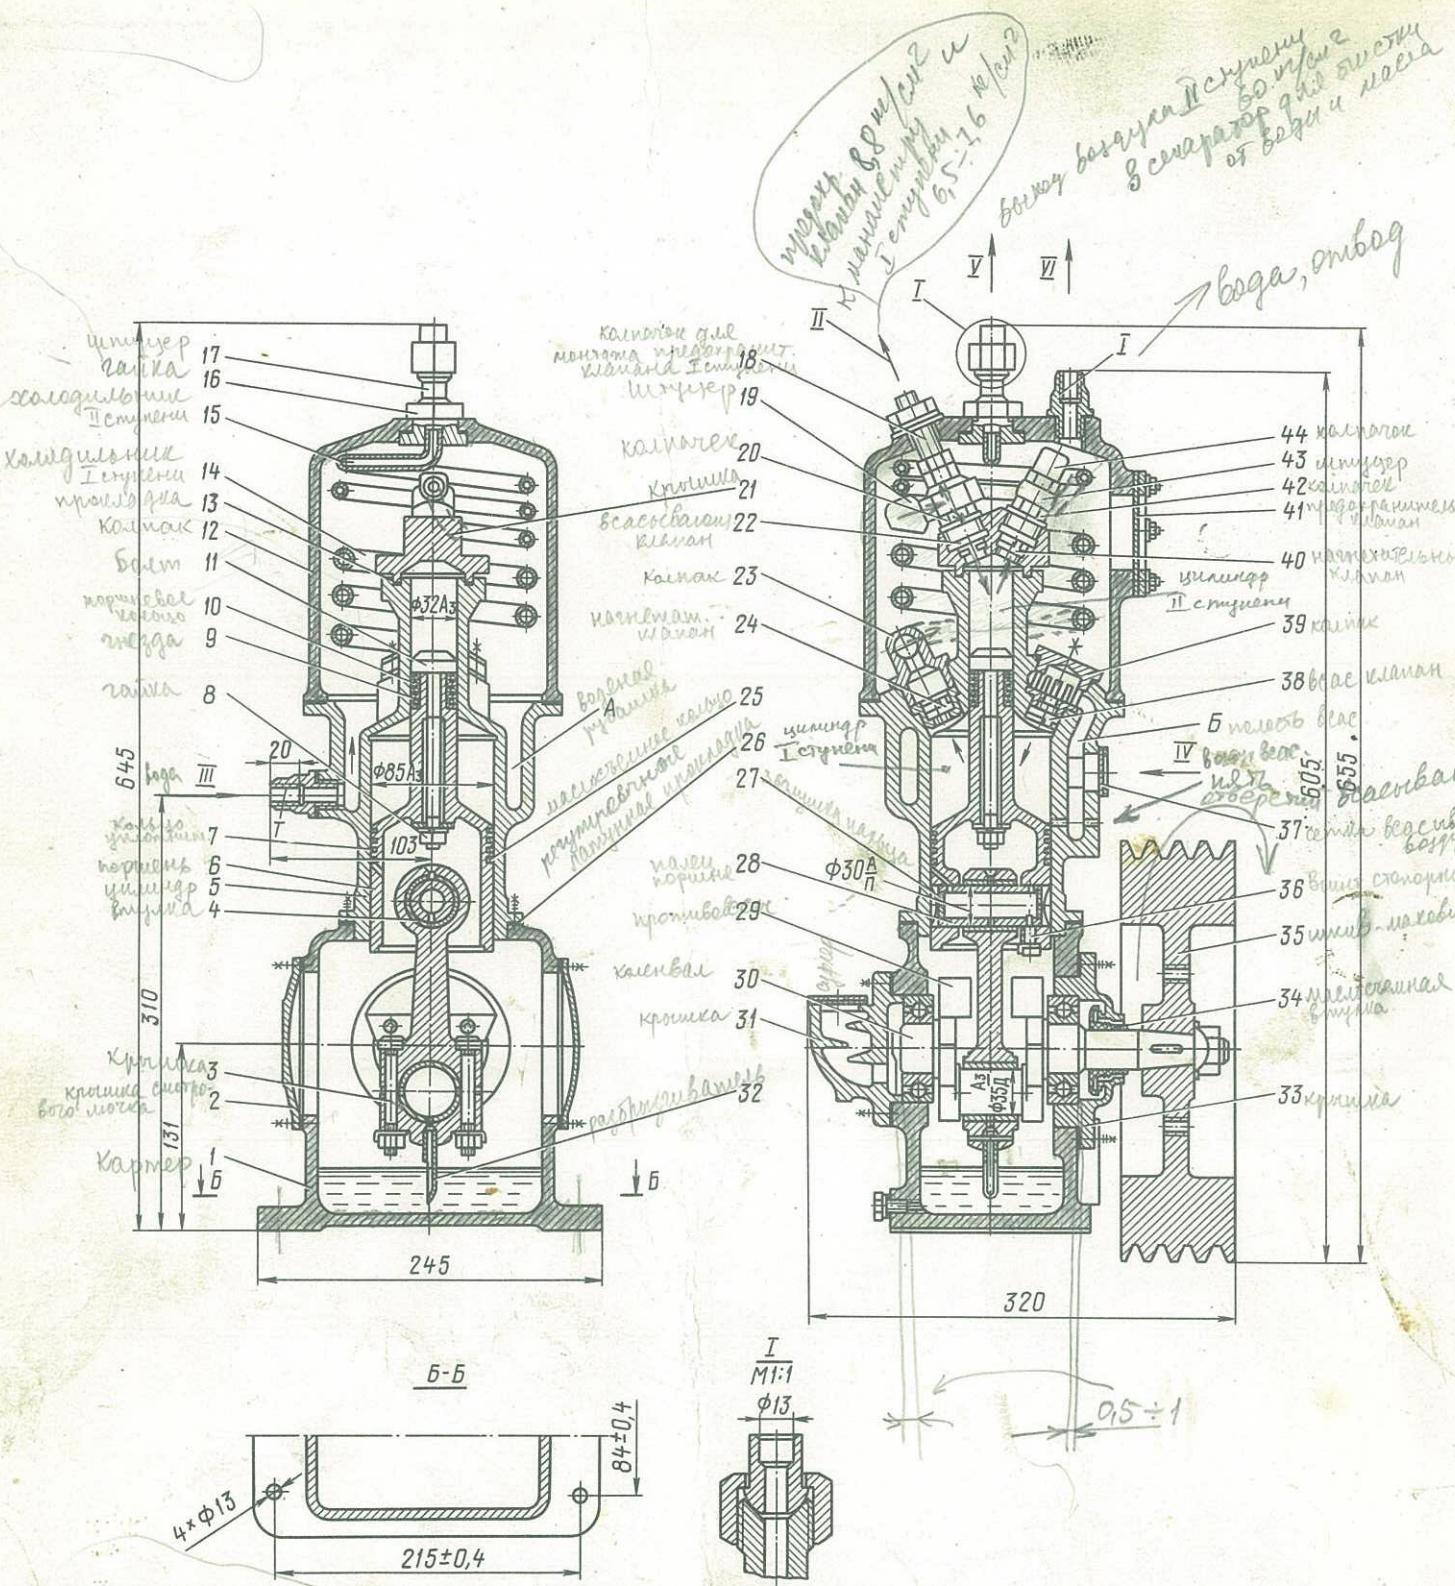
Компрессор КВД (разрез): 1- отвод ведра и компрессора
